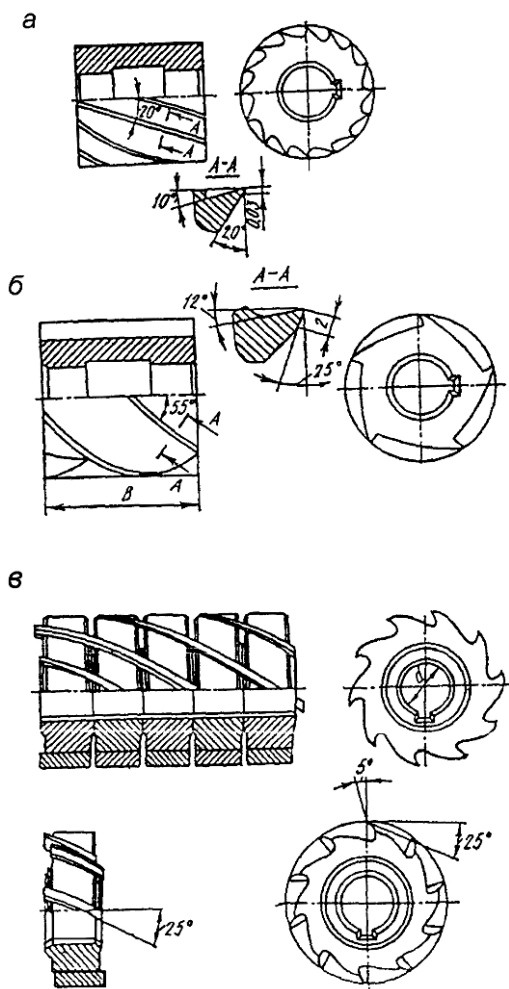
Фрезы для обработки широких поверхностей деталей
